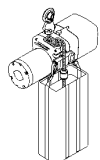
Cambio de la cadena sin cadena en el motor izador
